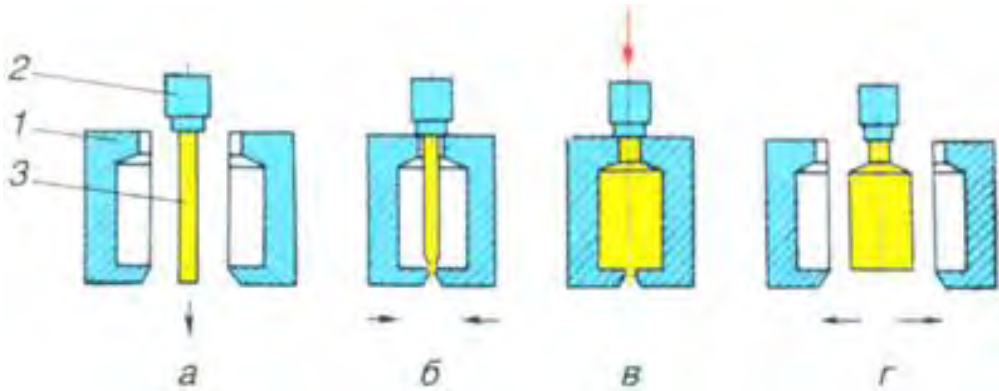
, а. Схема экструзионно-раздувного формования: 1 - пресс-форма; 2 - трубная головка; 3 - трубная заготовка
